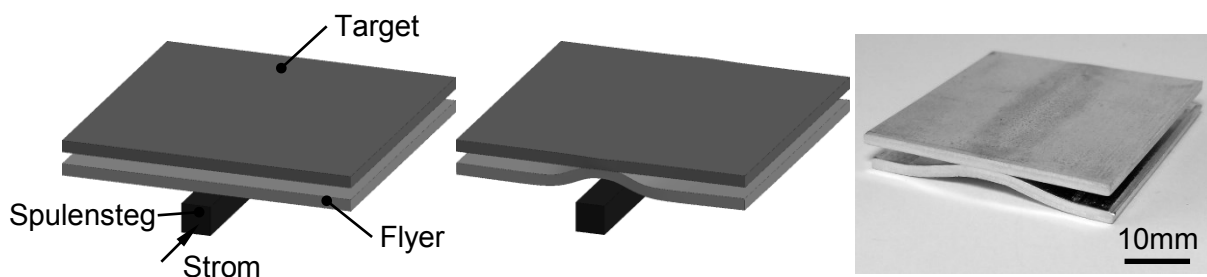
Schematischer Aufbau für das elektromagnetische Pulsschweißen. Links: vor dem Schweißen. Mitte: nach dem Schweißen. Rechts: Foto der Schweißprobe.
